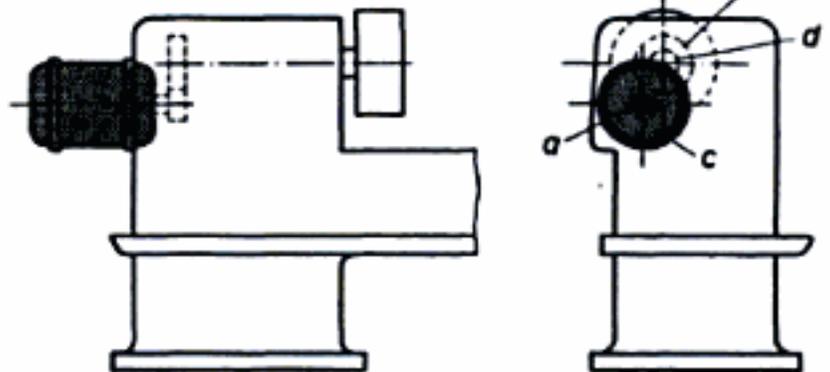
,3 Motor embridado; transmisión de fuerza por medio de ruedas dentadas: a) árbol motor; b) rueda dentada, c) motor de bridas; d) husillo de trabajo
